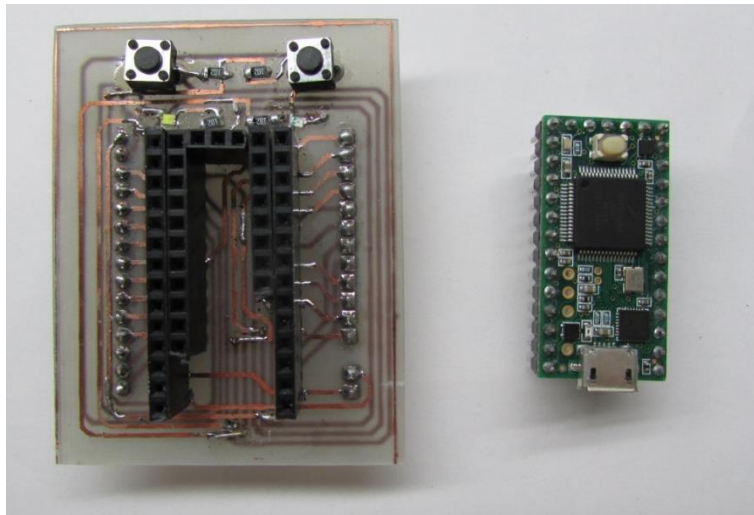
Pcb módulo de la tarjeta Teensy y tarjeta Teensy
